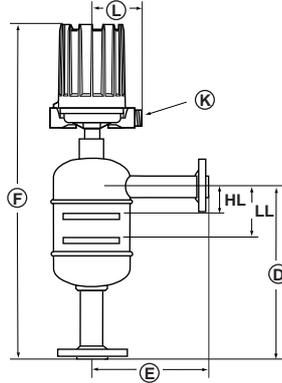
B75 mit Flanschschluß Ausführung seitlich/seitlich
